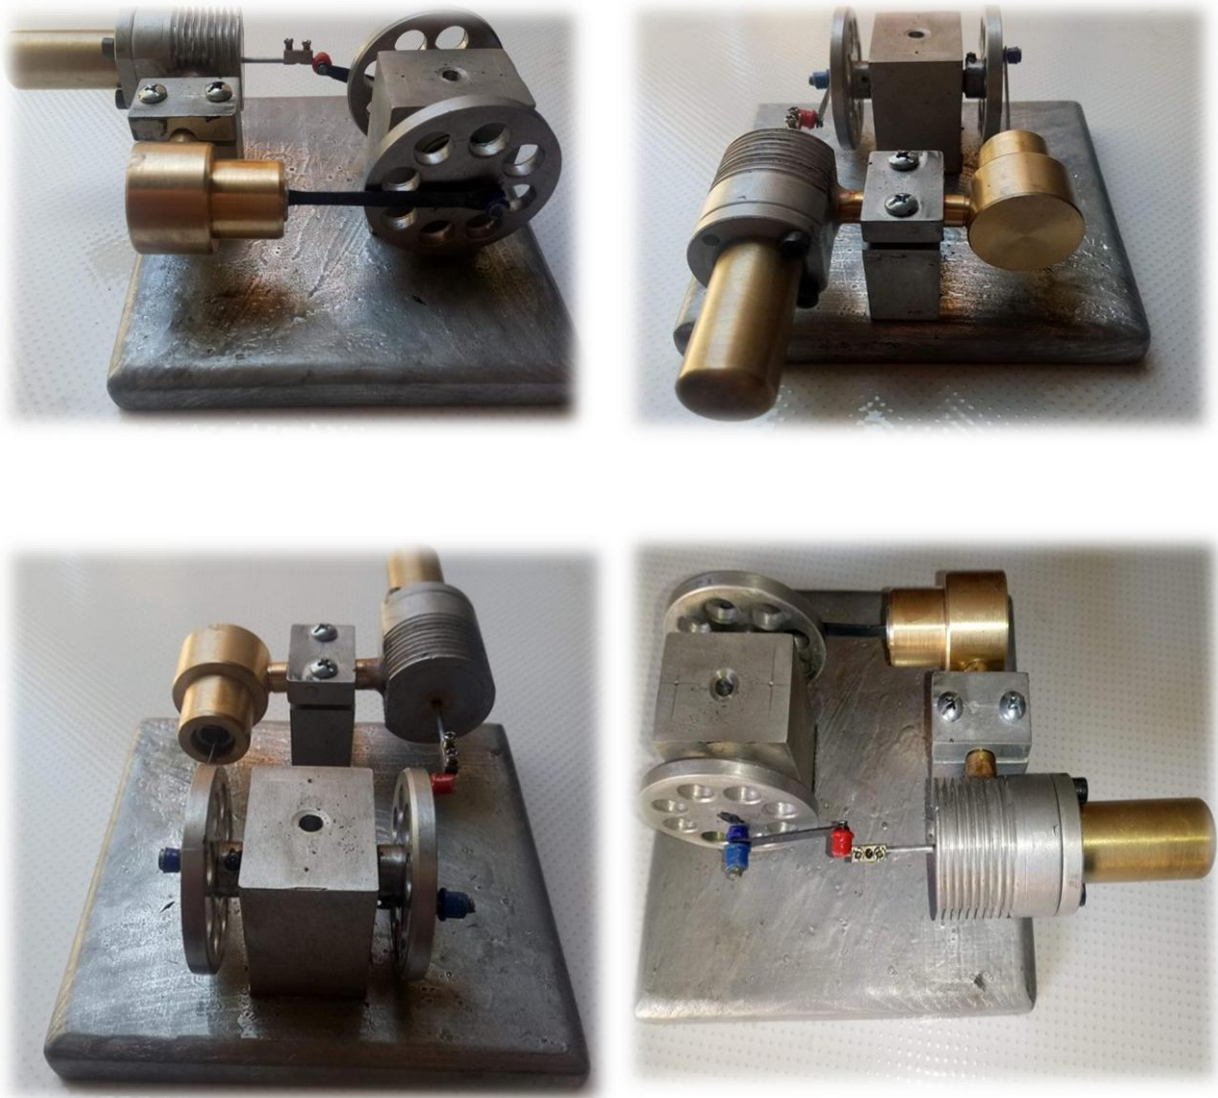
Le moteur de Stirling après l'assemblage.
